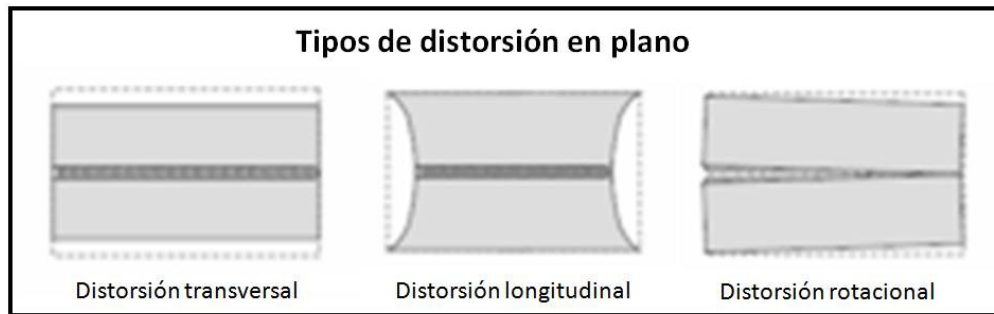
Muestra las variantes de distorsión en un plano. [2]
